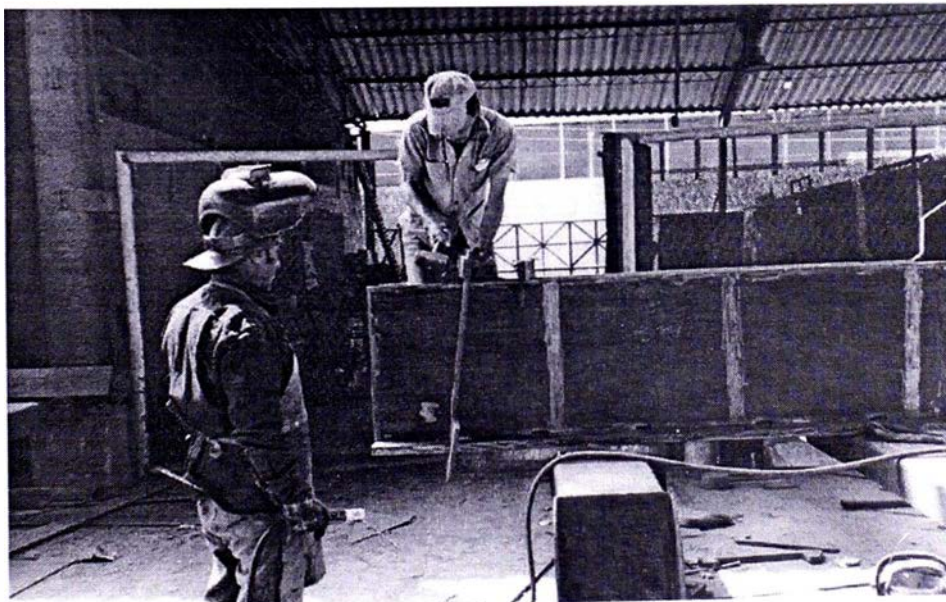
Ensamblaje de un miembro de la Brida Superior
